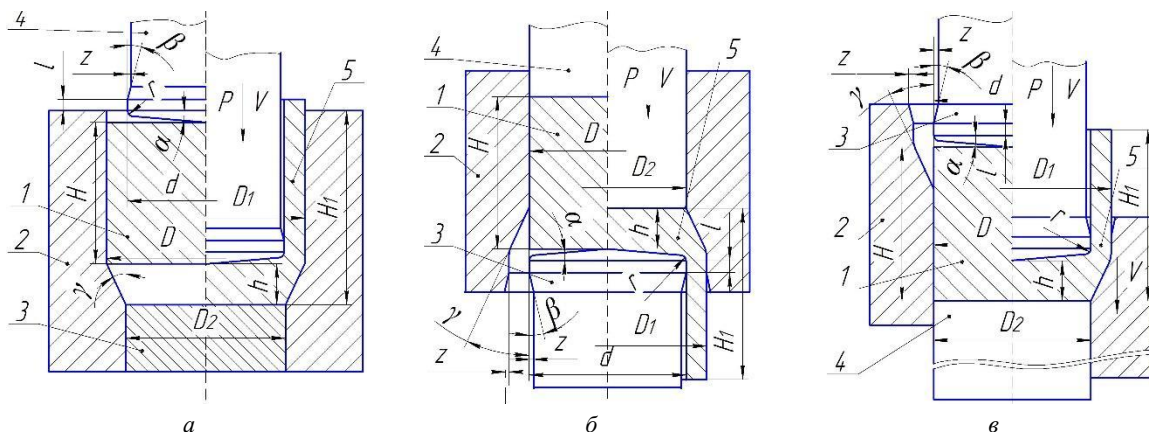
Схеми видавлювання порожнистих напівфабрикатів: а – схема зворотного видавлювання, б – схема прямого видавлювання з роздачою, в – схема зворотного видавлювання з роздачою
